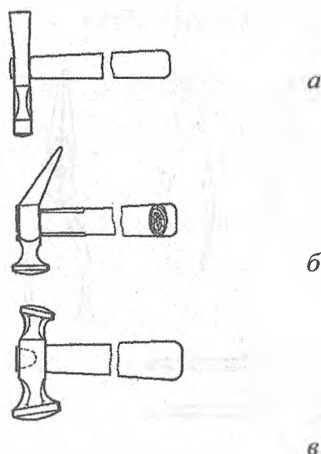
Обувные молотки: *а* – заготовочный; *б* – сапожный; *в* – плиточный
